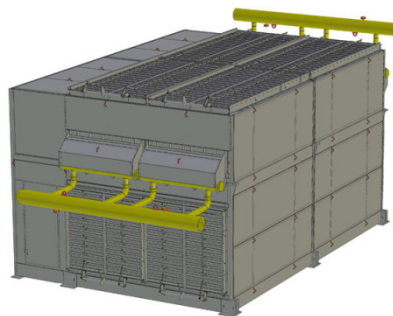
АВО блочного типа (БМР) [21, 49]
